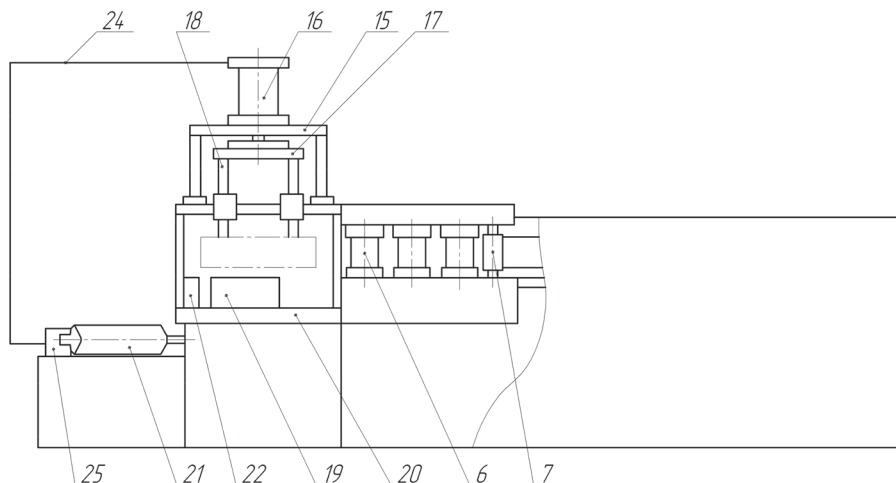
Принципиальная схема стана для прокатки заготовок малолистовых рессор автомобилей МАЗ (вид сбоку)
